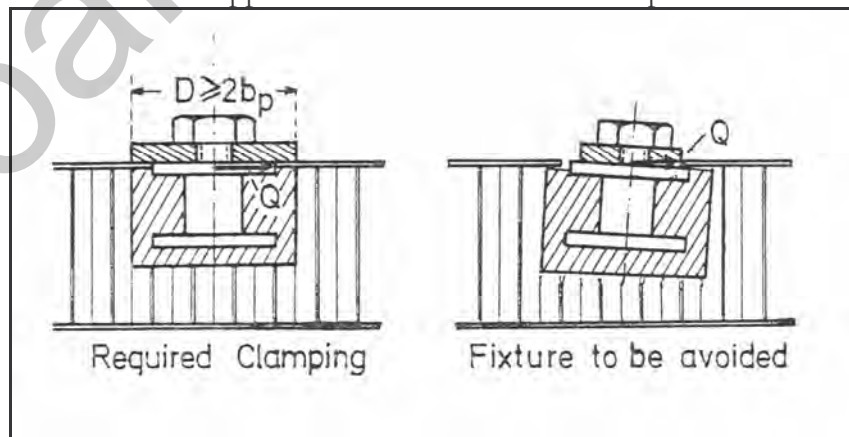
Montaggio corretto (a sinistra) ed errato (a destra) di un inserto caricato a taglio
